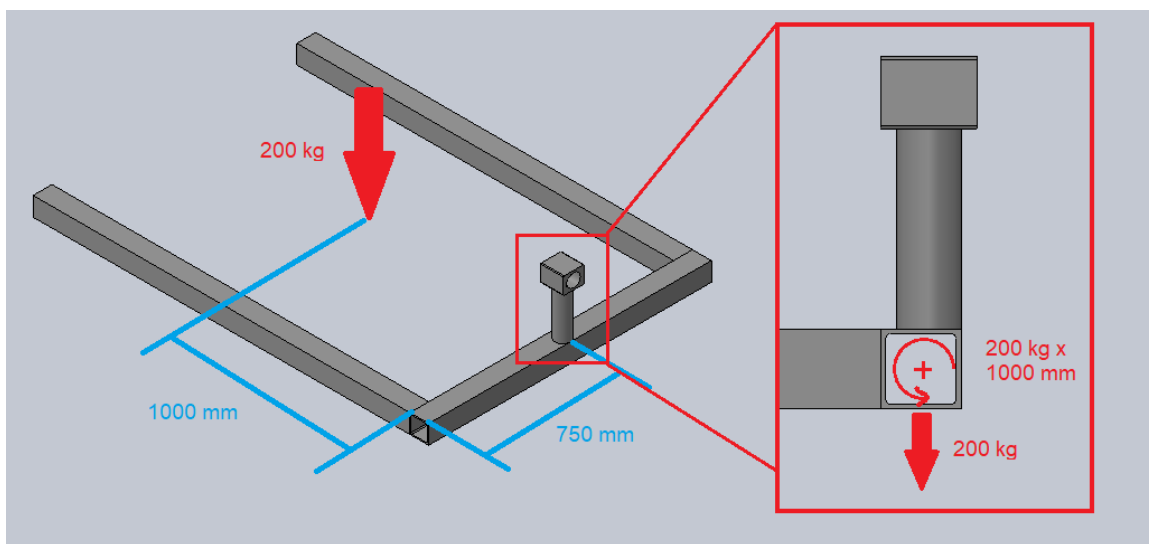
Dimensiones adoptadas para el cálculo de la horquilla y eje soporte.
